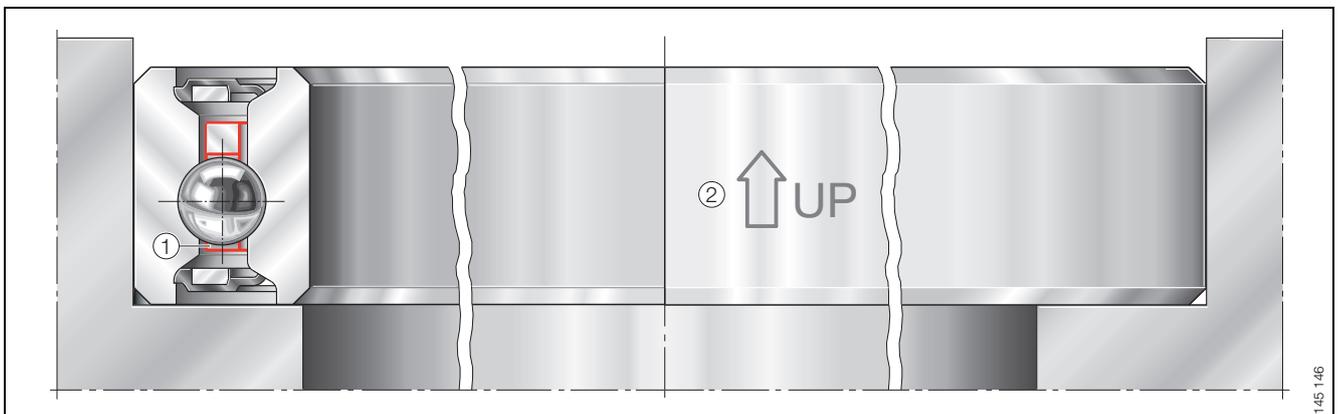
· Kennzeichnung der Käfigposition bei abgedichteten Dünnringlagern
